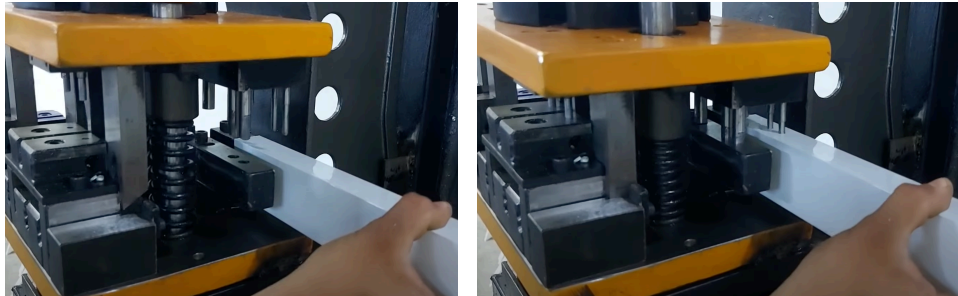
Se coloca la pieza y se baja la prensa con los troqueles (los punzones)
